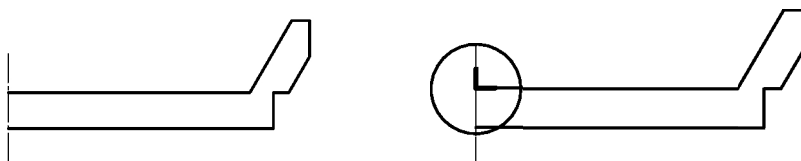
Эскизы для формирования 3D модели основания корпуса
